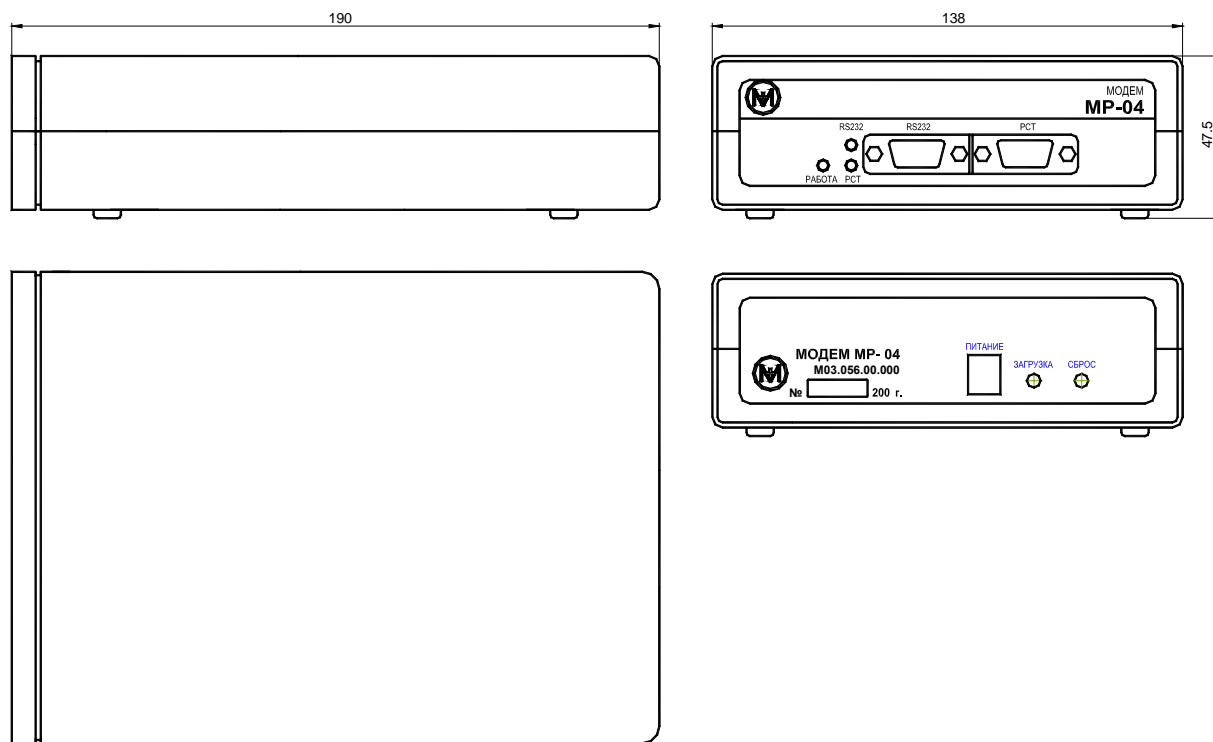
Внешний вид и габаритные размеры модема МИР МР-04.00
